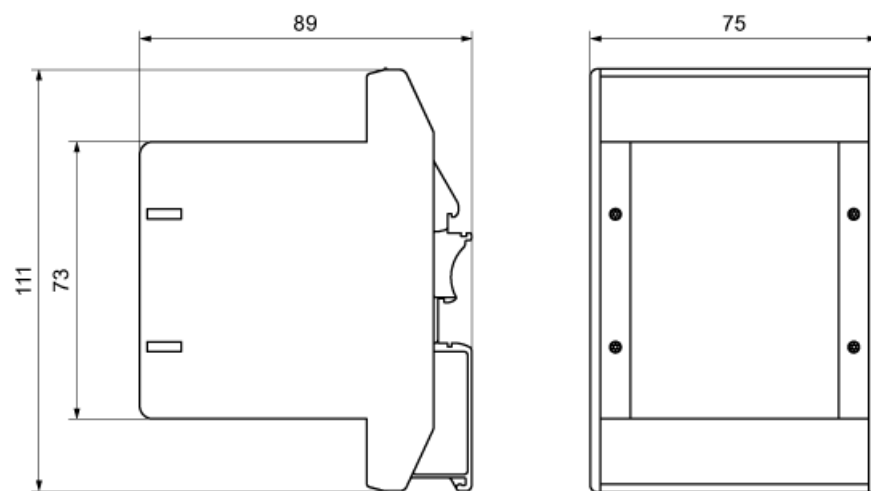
Safe Brake Adapter 外形尺寸图（单位 mm）
